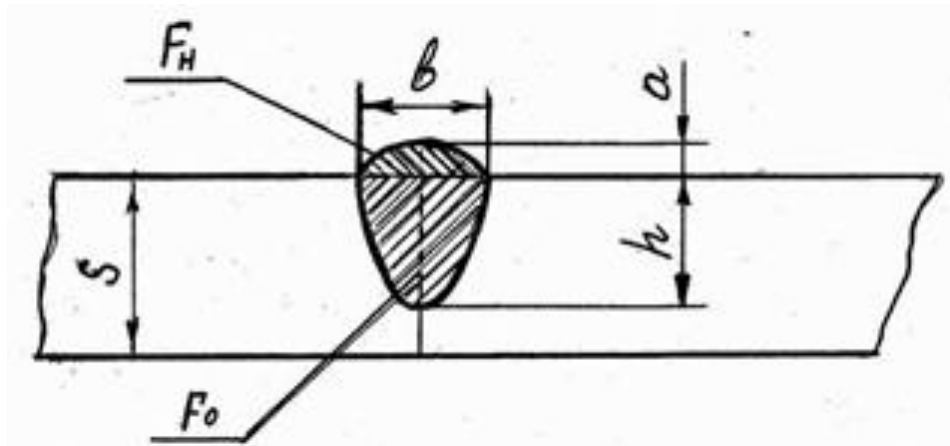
а – Основні геометричні розміри стикового шва при однібічному зварюванні
